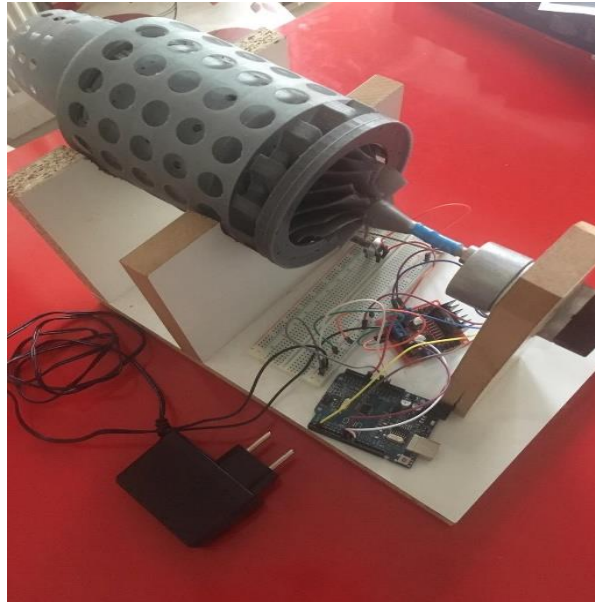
Turbojet Motoru Bileşenlerinin 3D Çıktılarının Montajlanmış Son Hali
